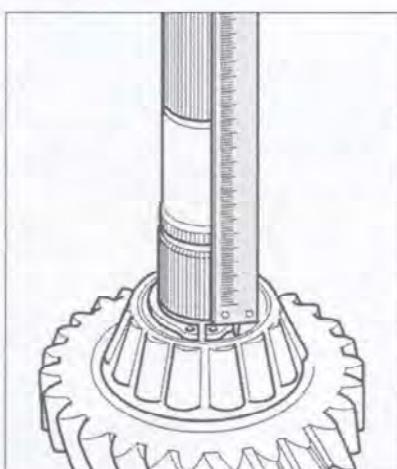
Штангенциркулем определите зазор между внутренней обоймой роликоподшипника и стопорным кольцом.
